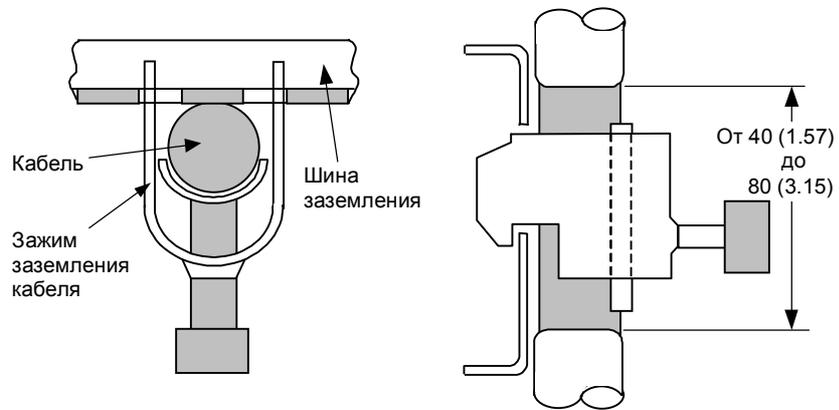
Конструкция зажима для заземления кабеля A99L-0035-0001
